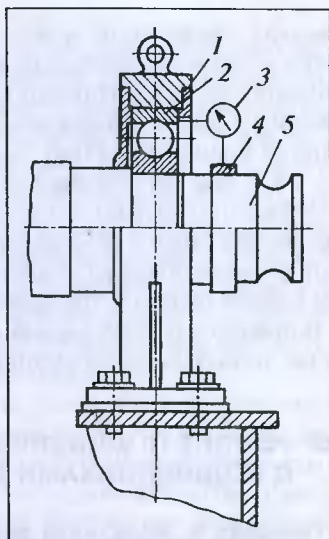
Проверка осевого биения наружного кольца шарикоподшипника:
